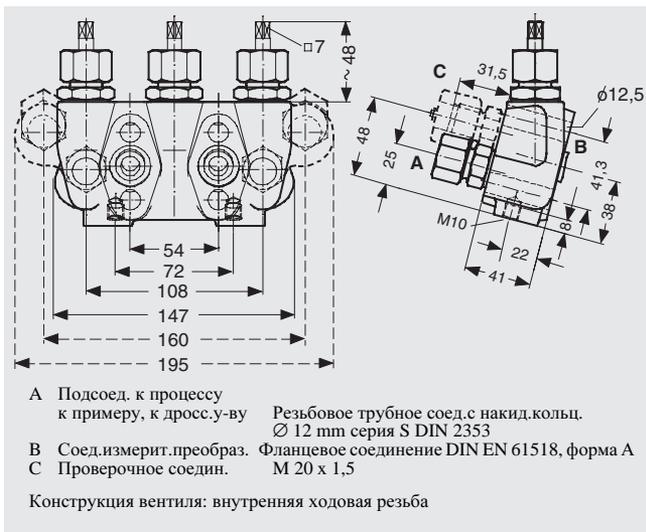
/92 Трехходовой вентильный блок DN 8 с резьбовым трубным соединением, размеры в мм
